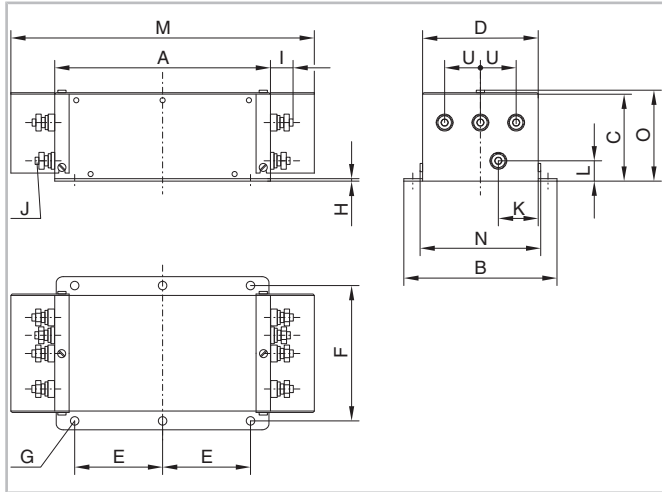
Габаритный чертеж RFI фильтра 3259-250-28
